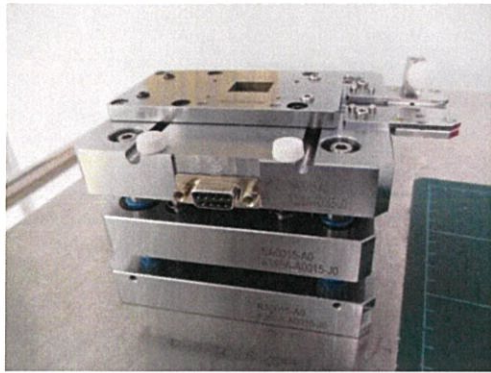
(ก) แสดงด้านหน้าเครื่องมือ Cutting Tool
